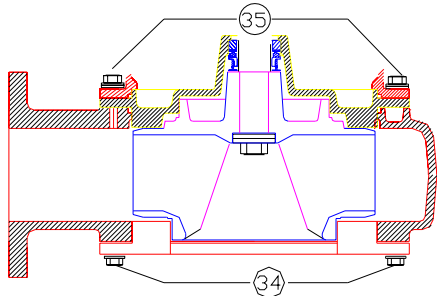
↑ Desmontaje de la carcasa de una bomba
